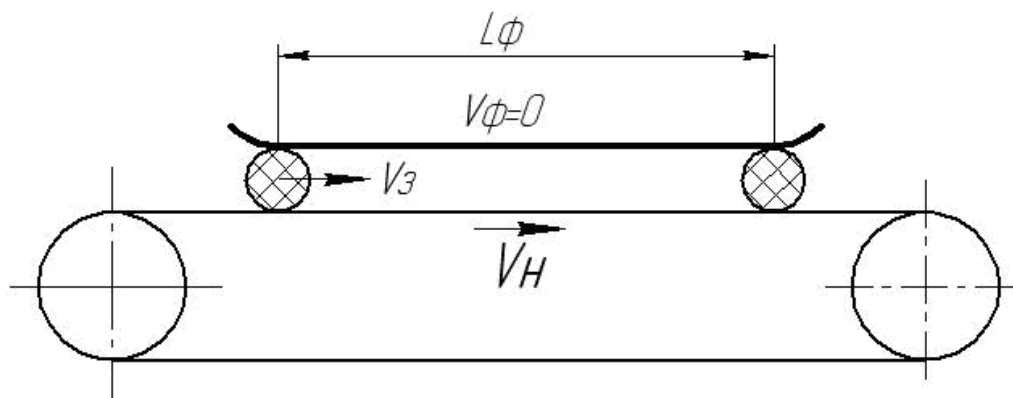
Визначення зони закатування тістової заготовки
